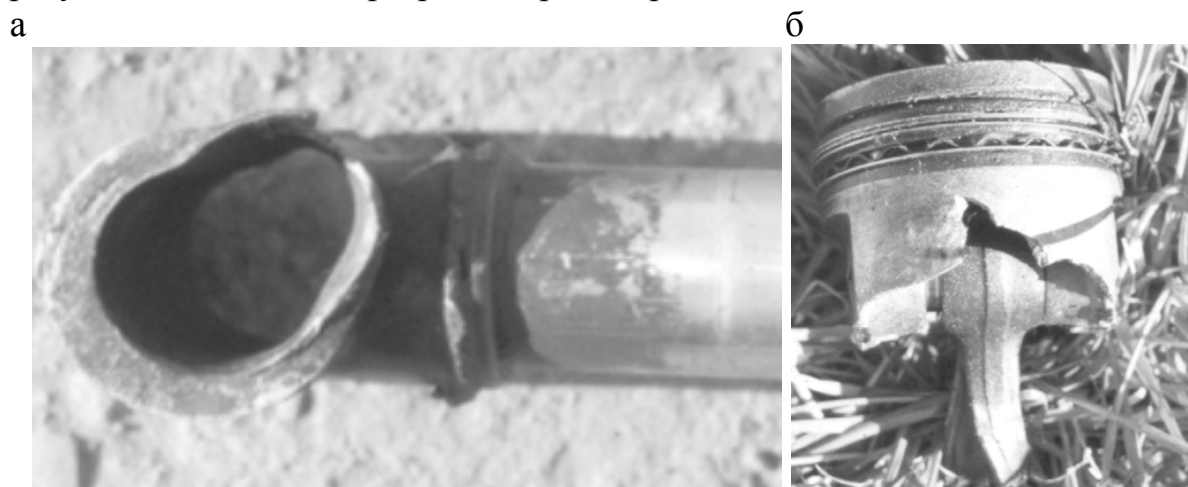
Пластическое разрушение (разрыв) проушины штока поршня гидроцилиндра (а) и хрупкое разрушение поршня двигателя (б)
